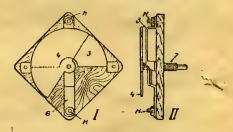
Вид сверху и разрез готового самодельного однопластинчатого конденсатор:
